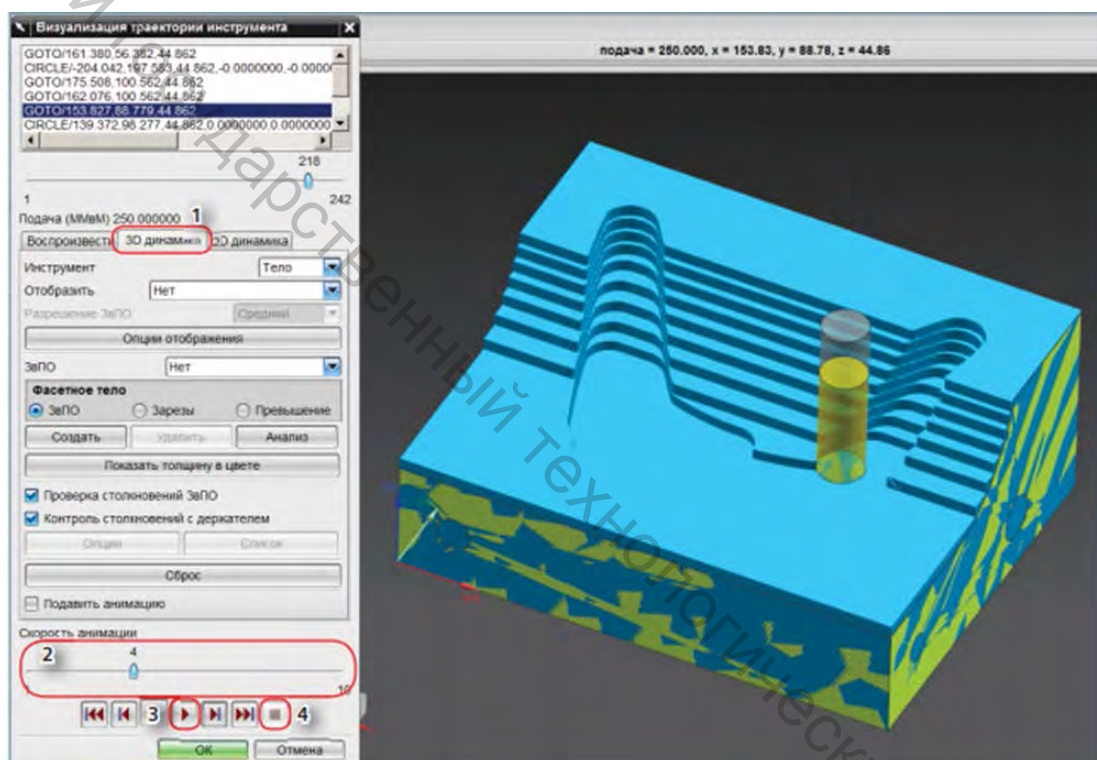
Вкладка верификации обработки при глубинном фрезеровании и её результат в графической области
